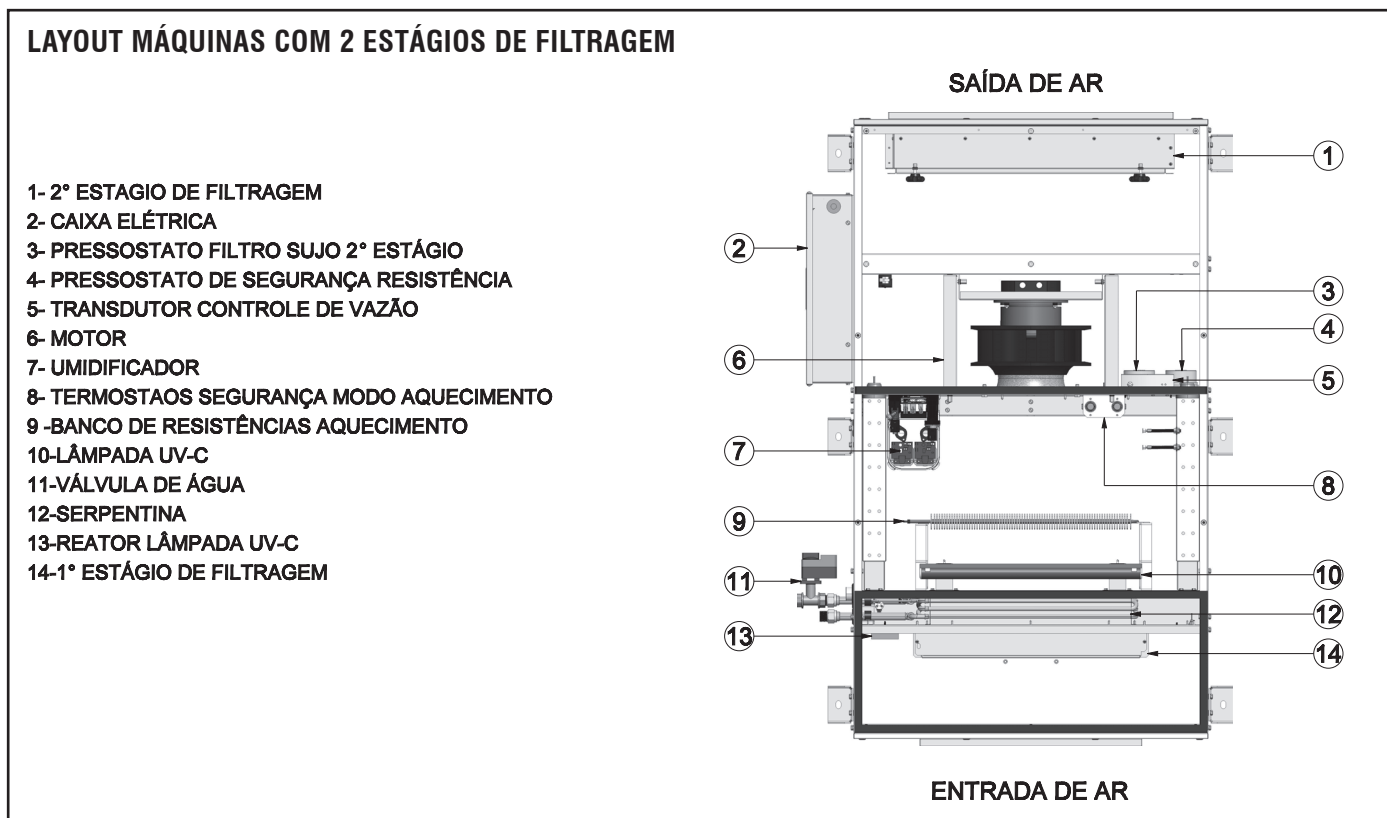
LAYOUT DOS COMPONENTES E OPCIONAIS: MÁQUINAS COM 2 ESTÁGIOS DE FILTRAGEM
